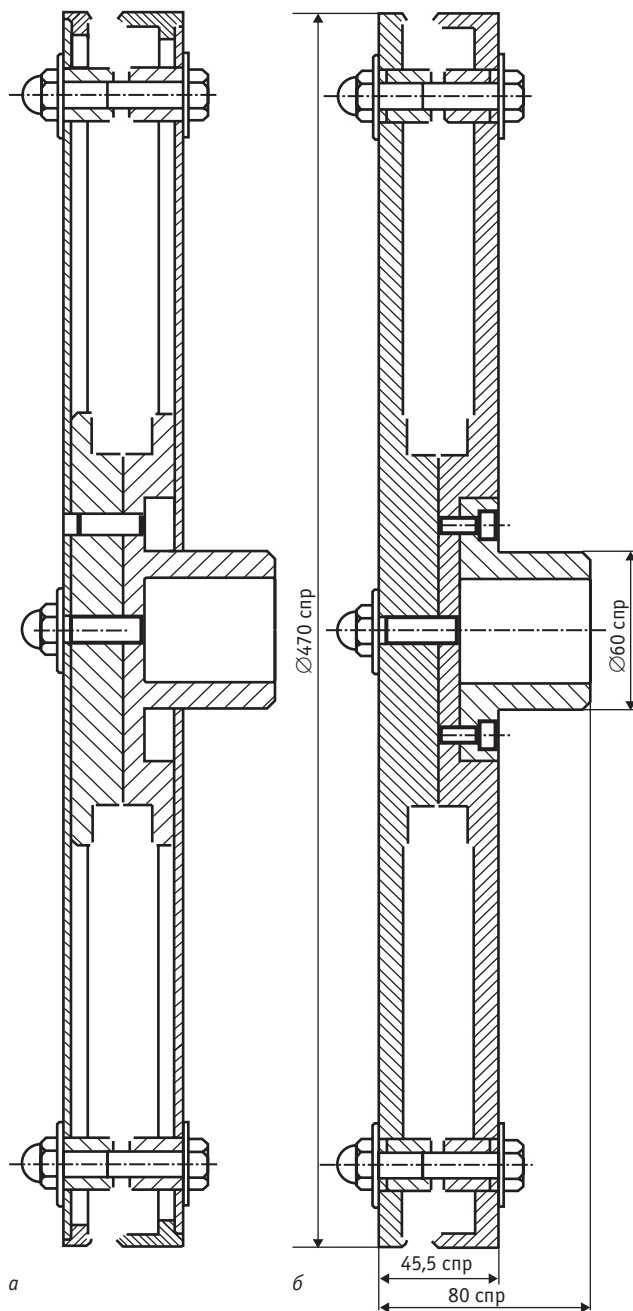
Защитное приспособление: а – базовая конструкция; б – усовершенствованная конструкция приспособления
